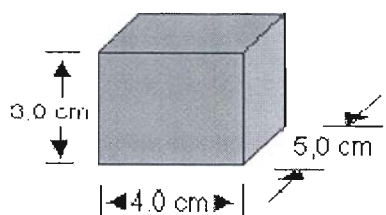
apoio para a base do kit experimental. Ele deve ser fixado à base com pregos.
